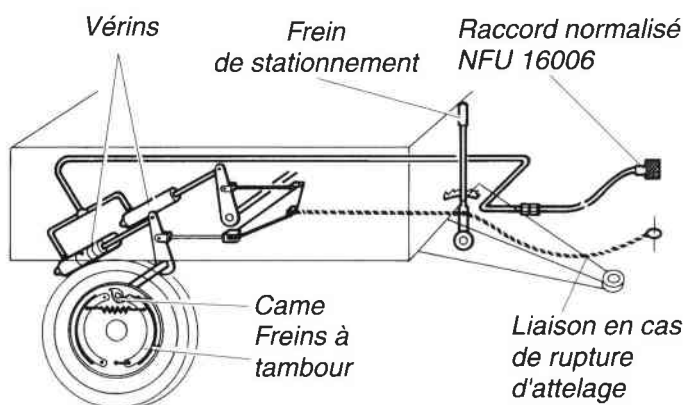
Le principe du freinage hydraulique d'une remorque
